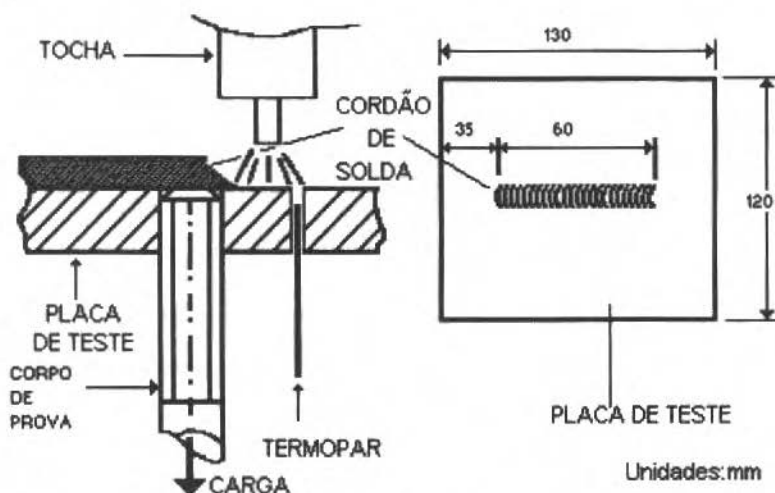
Ajuste do Corpo de Prova à Placa de Teste e Dimensões da Placa de e do Cordão de Solda utilizados neste Trabalho
